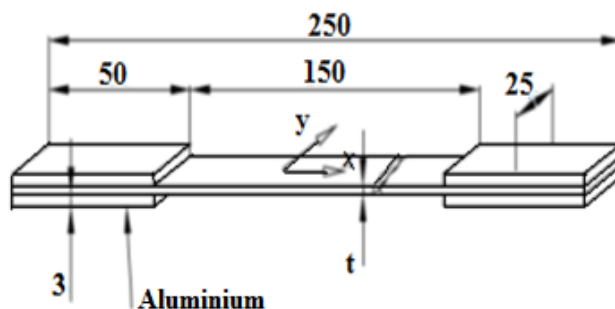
Géométrie et dimensions des éprouvettes testées exprimées en mm
